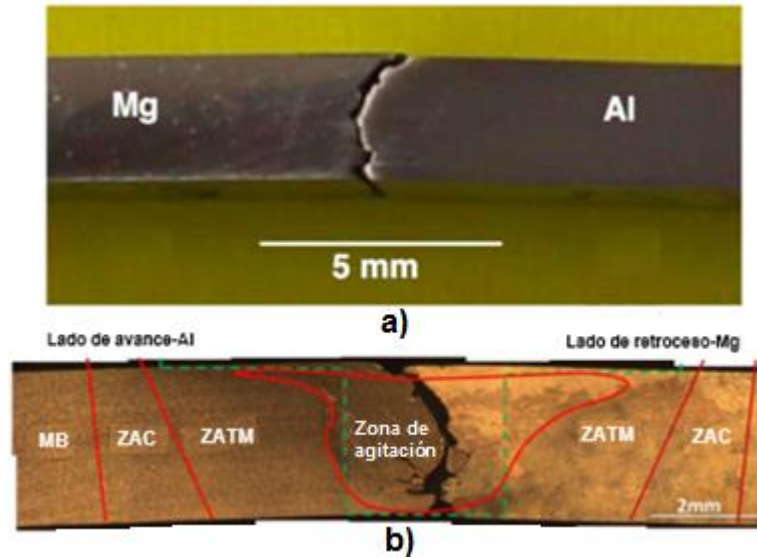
Unión soldada con 1400 rpm y 500 mm/min fracturada después de la carga de tensión, a) macrografía, b) muestra observada con el microscopio óptico (37).
